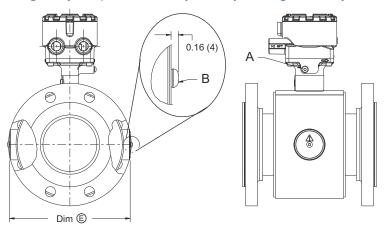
Sensores MS com flanges de pescoço soldado de 3 pol. a 36 pol. e largura de corpo com a opção M2
